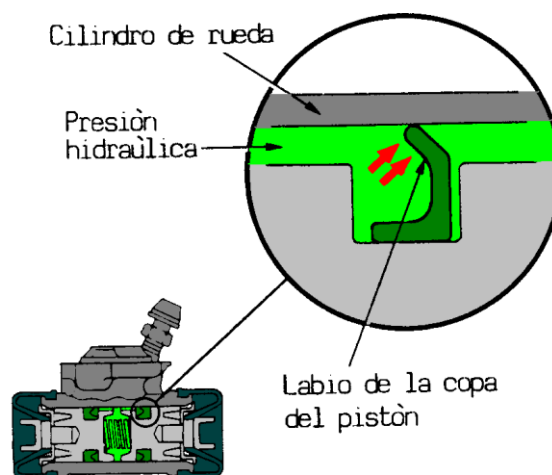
Cilindro de rueda de tambor aplicado.
